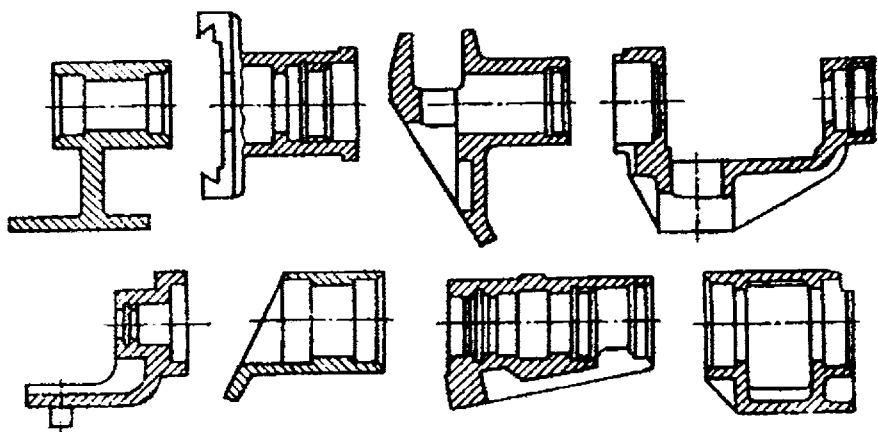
Группа заготовок, обрабатываемых с одной наладки
